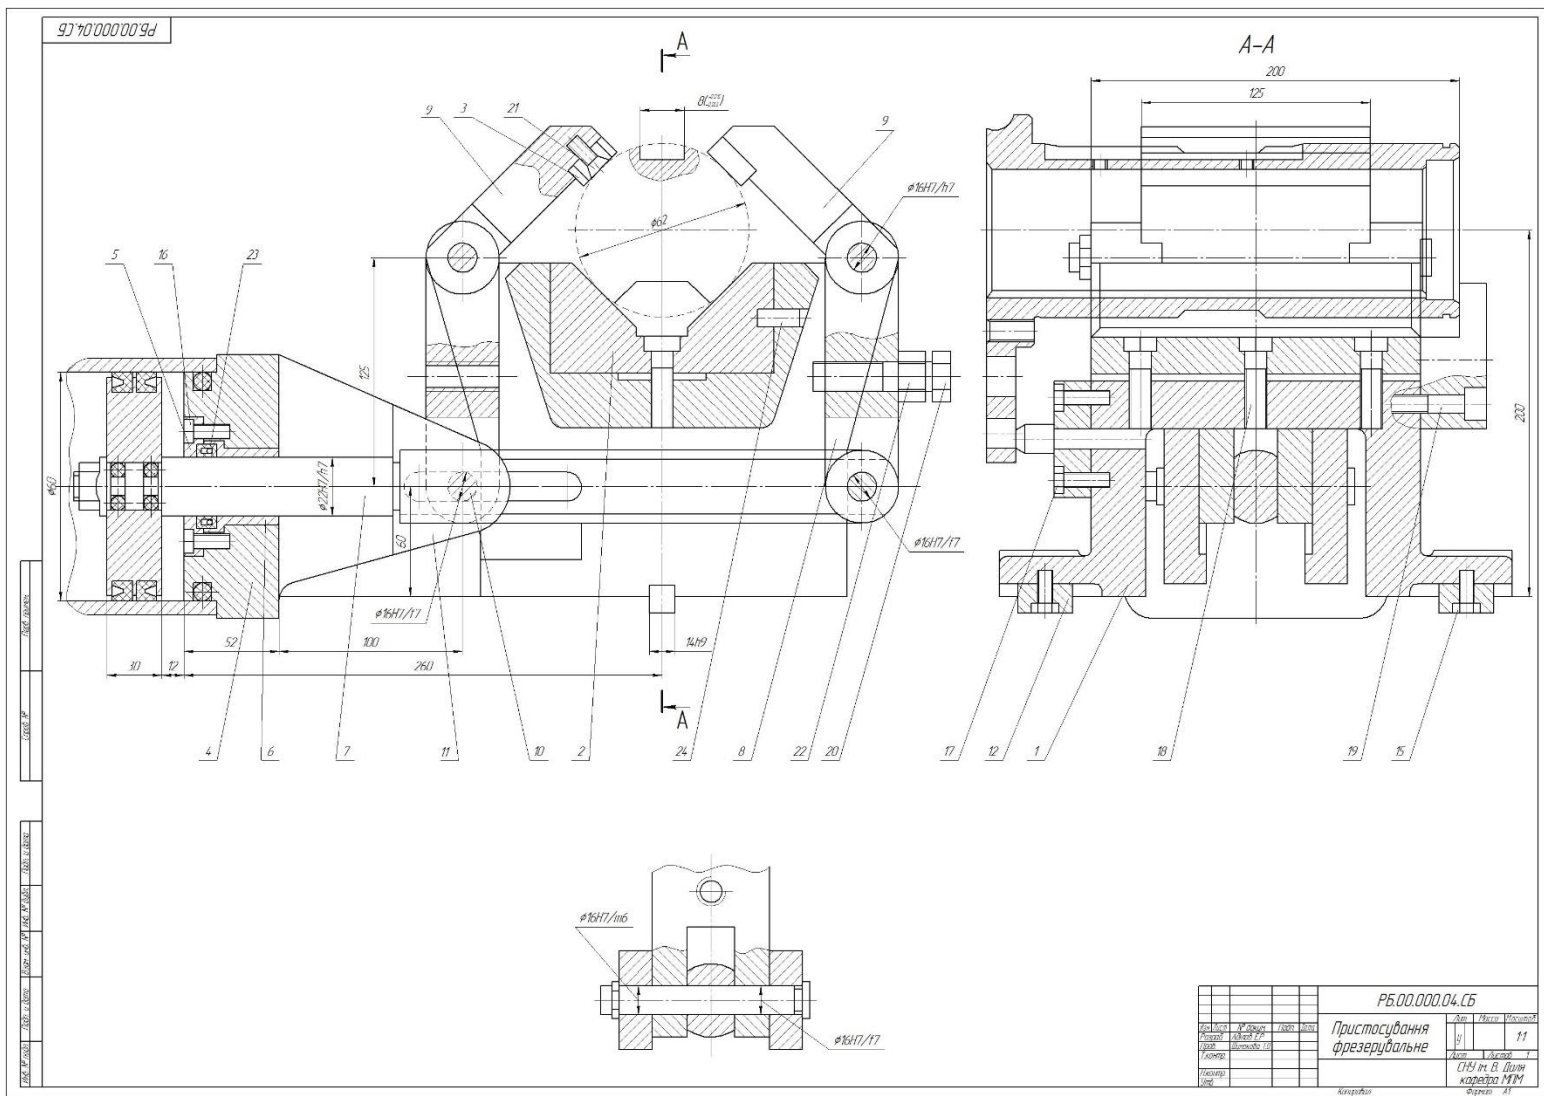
Кресленик верстатного пристосування для виконання операції фрезерування шпонкового пазу
